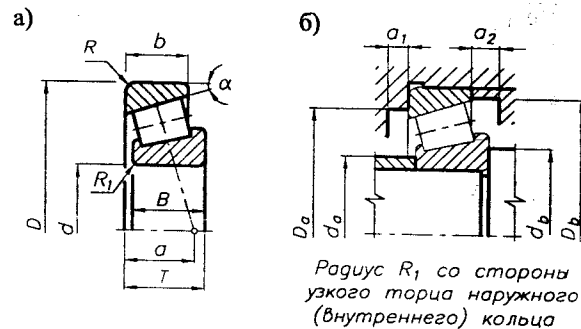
Габаритные и установочные размеры роликовых конических однорядных подшипников
